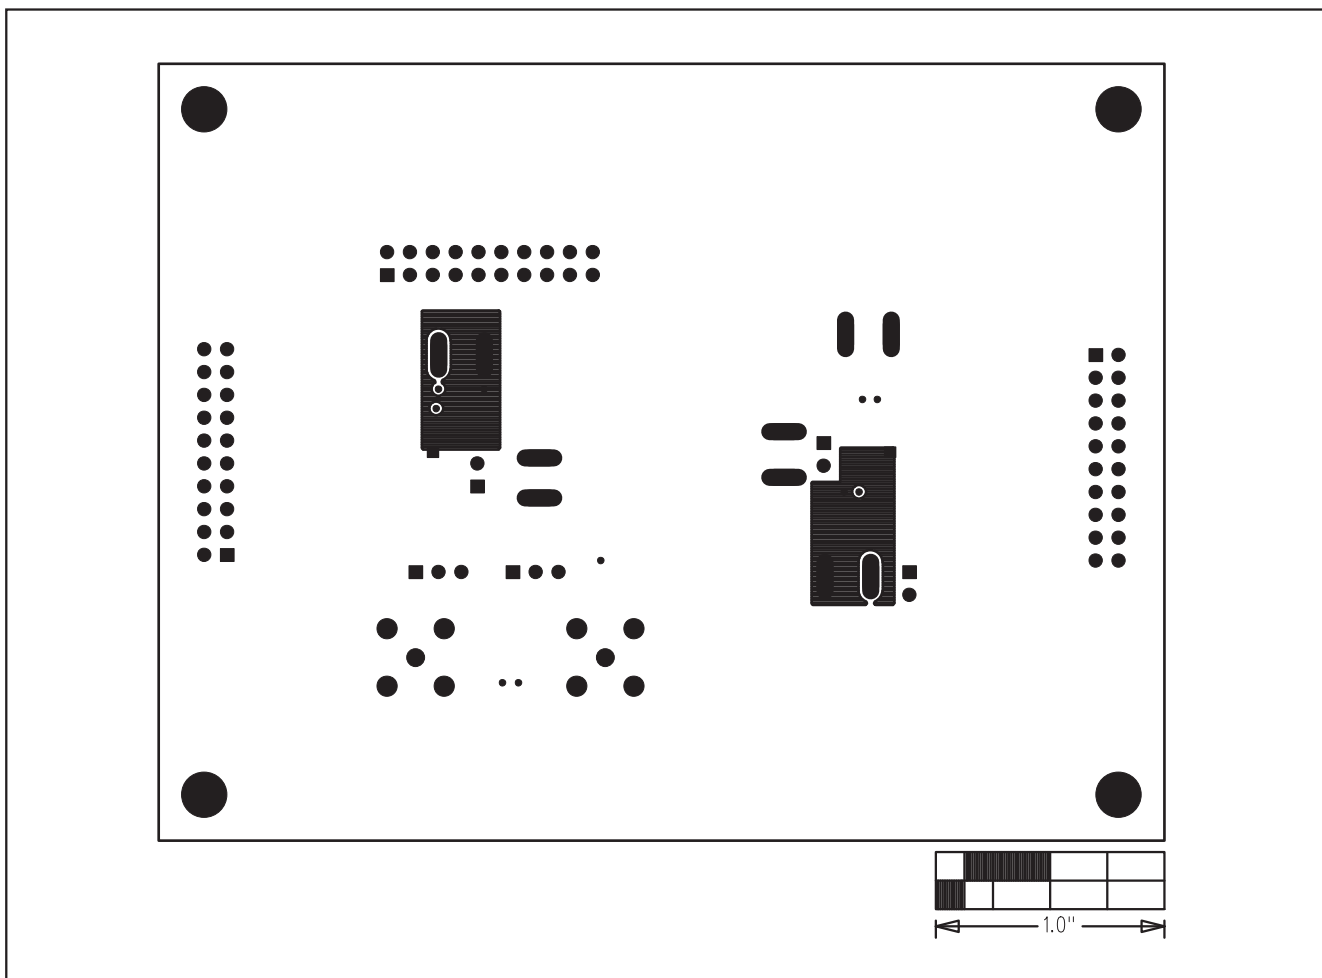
MAX9225/6评估板PCB布局—焊接层
